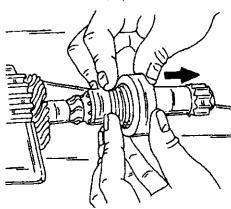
Снятие приводной шестерни стартера с вала якоря.
